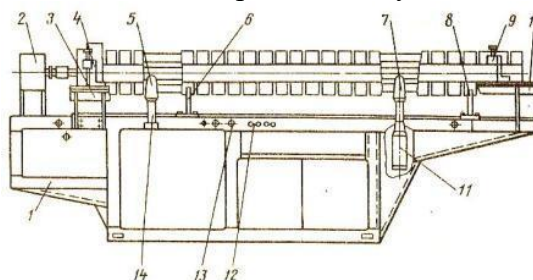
Стенд для разборки, сборки, обкатки подборщиков: 2) – *Откидывающийся привод вала*; 3) – *Передняя стойка*; 5) – *Наставки с призмами и прихватами*; 6) – *Неподвижные опоры*; 7) – *Наставки с призмами и прихватами*; 8) – *Неподвижные опоры*; 10) – *Задняя стойка*; 12) – *Ручки управления пневмоцилиндрами*; 13) – *Кнопки управления*.
